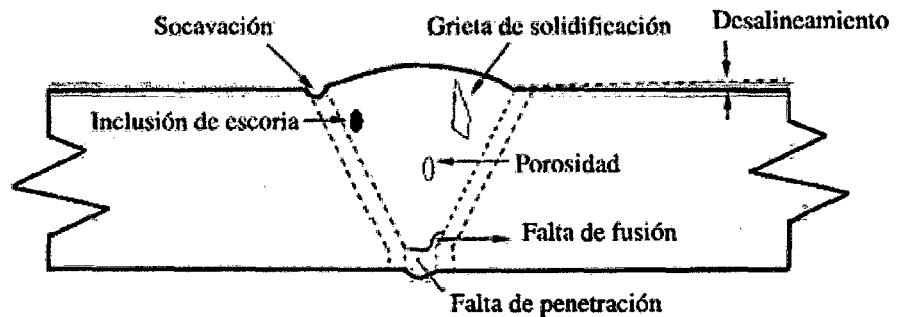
Tipo de discontinuidades en la soldadura. (Referencia Oxagasa, 2014, Manual del soldador, El Salvador ,88P).
